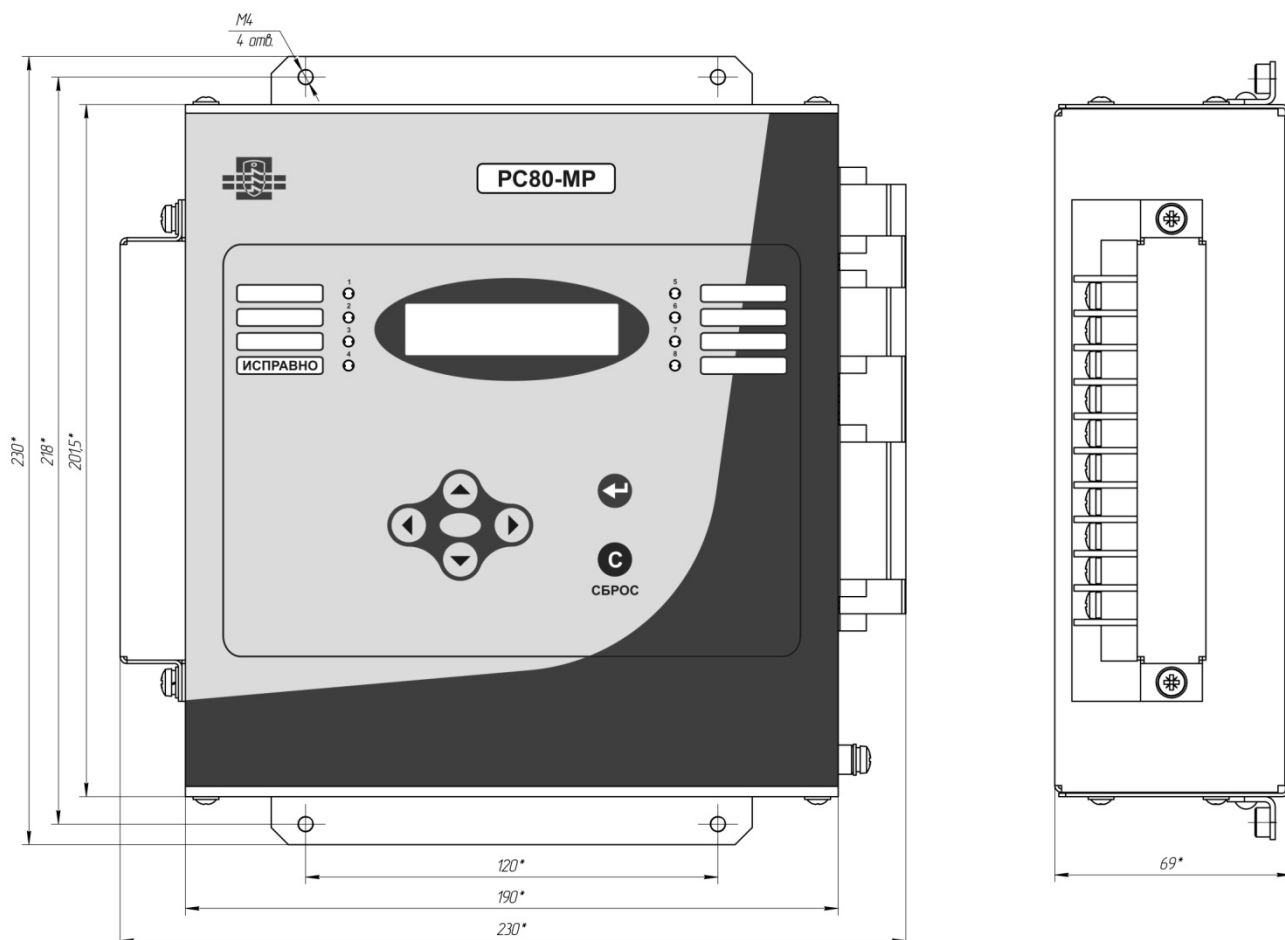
Габаритные и присоединительные размеры устройства РС80-МР
